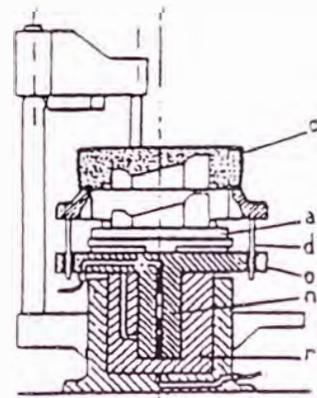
La misma máquina de la figura precedente. El plato está desviado lateralmente y la máquina en la fase de desmodelar.
